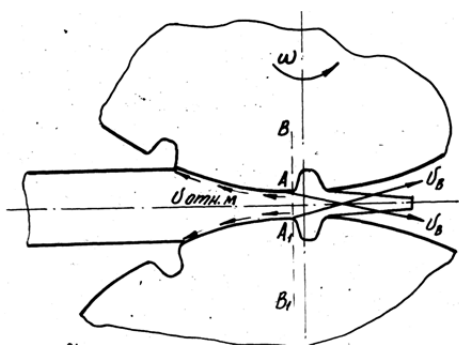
Схема очага деформации при периодической прокатке заготовки лопатки
